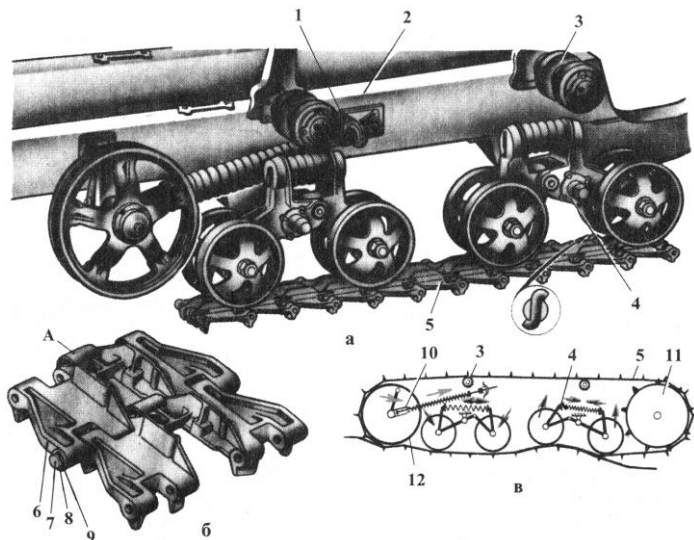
Гусеничний рушій: а – будова; б – ланки гусениці; в – схема; 1 – регулювальна гайка натяжного механізму; 2 – рама; 3 – підтримуючий ролик; 4 – балансир; 5 – гусениця; 6 – ланка; 7 – палець; 8 – шайба; 9 – шплінт; 10 – натяжний механізм; 11 – ведуча зірочка; 12 – напрямне колесо; А – цівка.
